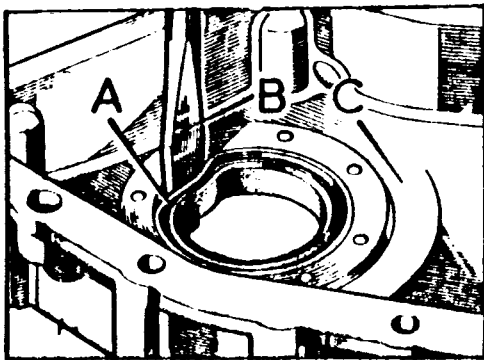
Desmontaje del retén delantero del cigueñal
